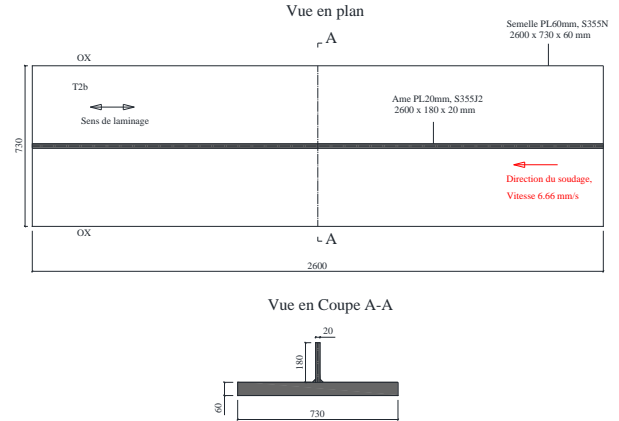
Vue en plan et coupe du soudage âme-semelle (dimensions en mm)
